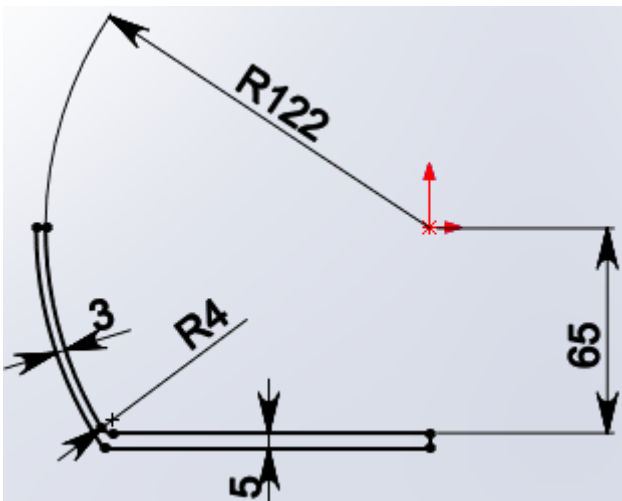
Сборочный чертеж «Сковорода»
